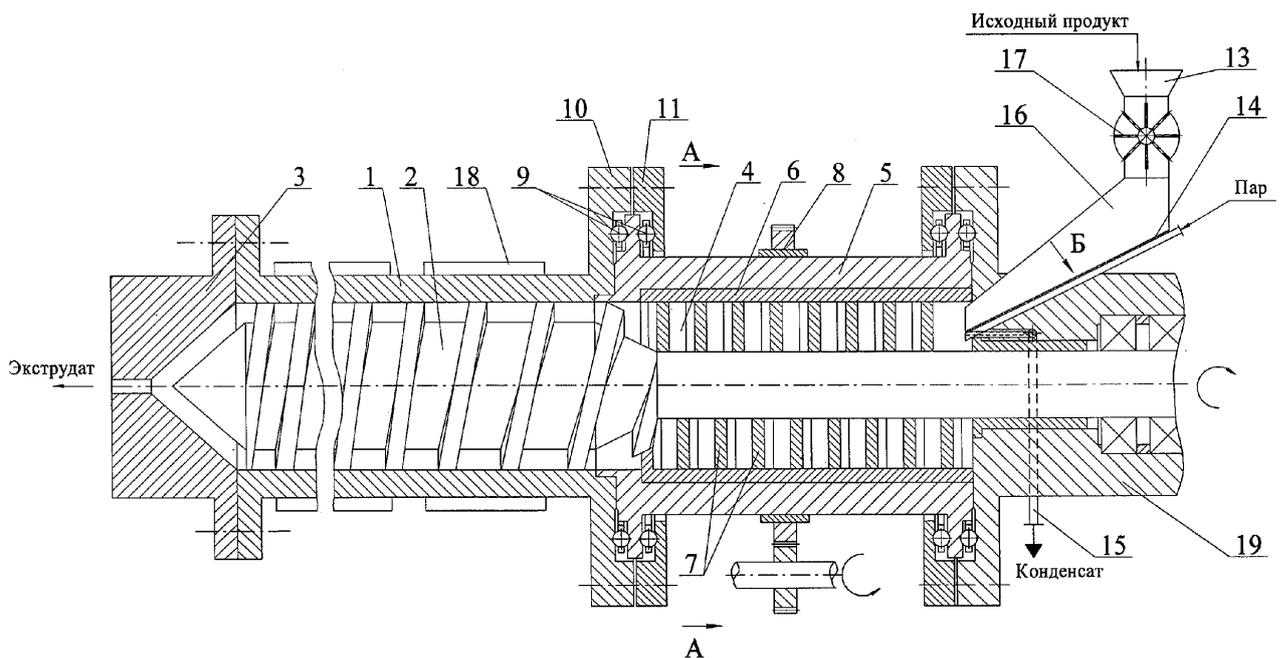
Экструдер: 1 – рабочая камера; 2 – шнек; 3 – матрица с формующими отверстиями; 4 – смеситель; 5 – корпус; 6 – цилиндрическая гильза; 7 – лопатки; 8 – венцовая шестерня; 9 – опорные подшипники; 10 – фланец; 11 – полукольцо; 12 – сепаратор; 13 – загрузочный бункер; 14 – наклонное двойное дно; 15 – трубка для отвода сконденсированного водяного пара; 16 – пропариватель; 17 – шлюзовый питатель; 18 – нагреватели; 19 – подшипниковый узел
